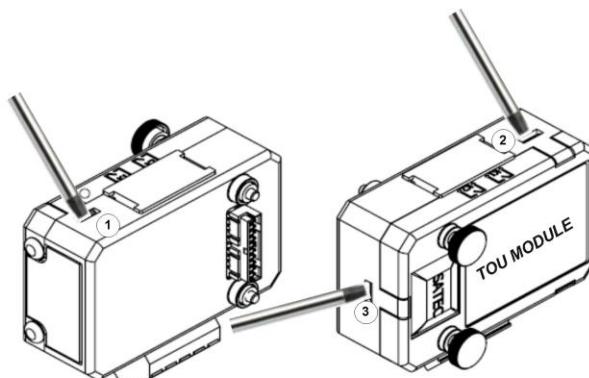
Положение защелок на корпусе дополнительного модуля
